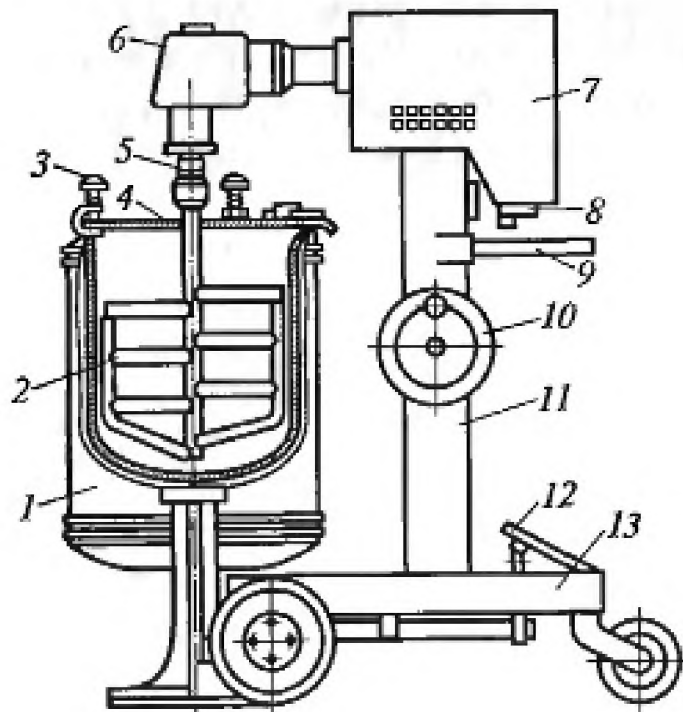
Машина МКП-60: 1 – котел; 2 – лопать; 3 – затискувач; 4 – кришка; 5 – муфта з’єднувальна; 6 – редуктор зубчастий конічний; 7 – привід; 8 – упор; 9 – рукоятка; 10 – маховик; 11 – колона телескопічна; 12 – пристрій фіксуючий; 13 – візок
